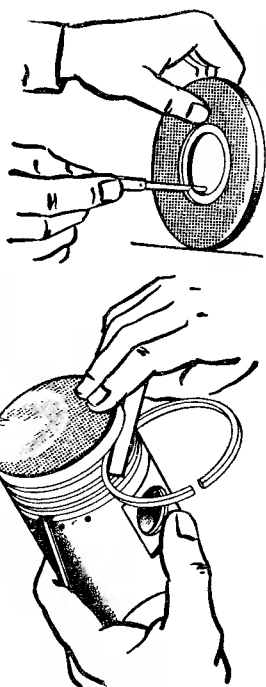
Проверка радиального и бокового зазоров, устанавливаемых поршневых колец
